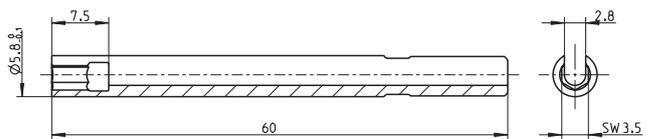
Montageschlüssel Typ 1300A125 für Kabel
